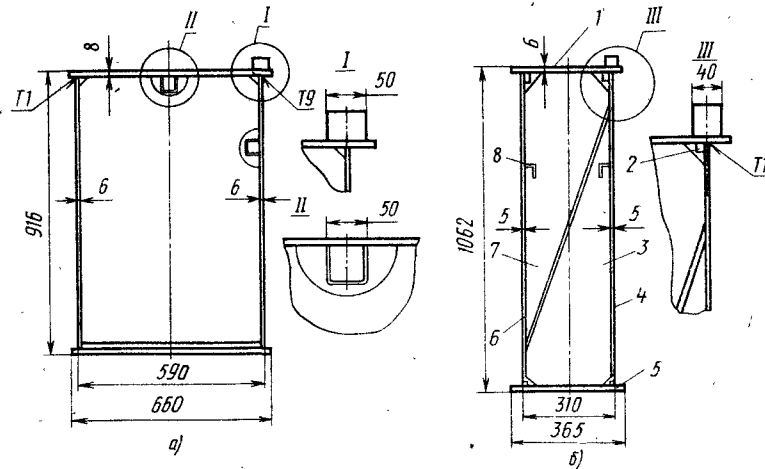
Балки с расположением подтележного рельса над стенкой:
